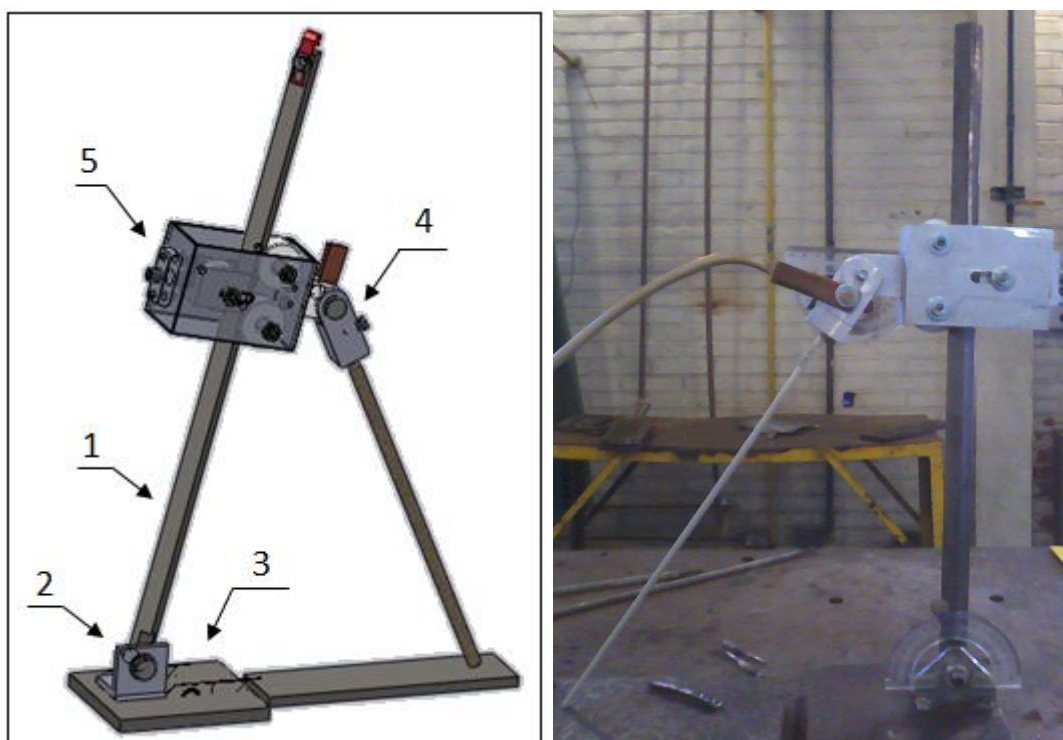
Dispositivo de soldagem por gravidade inicial
